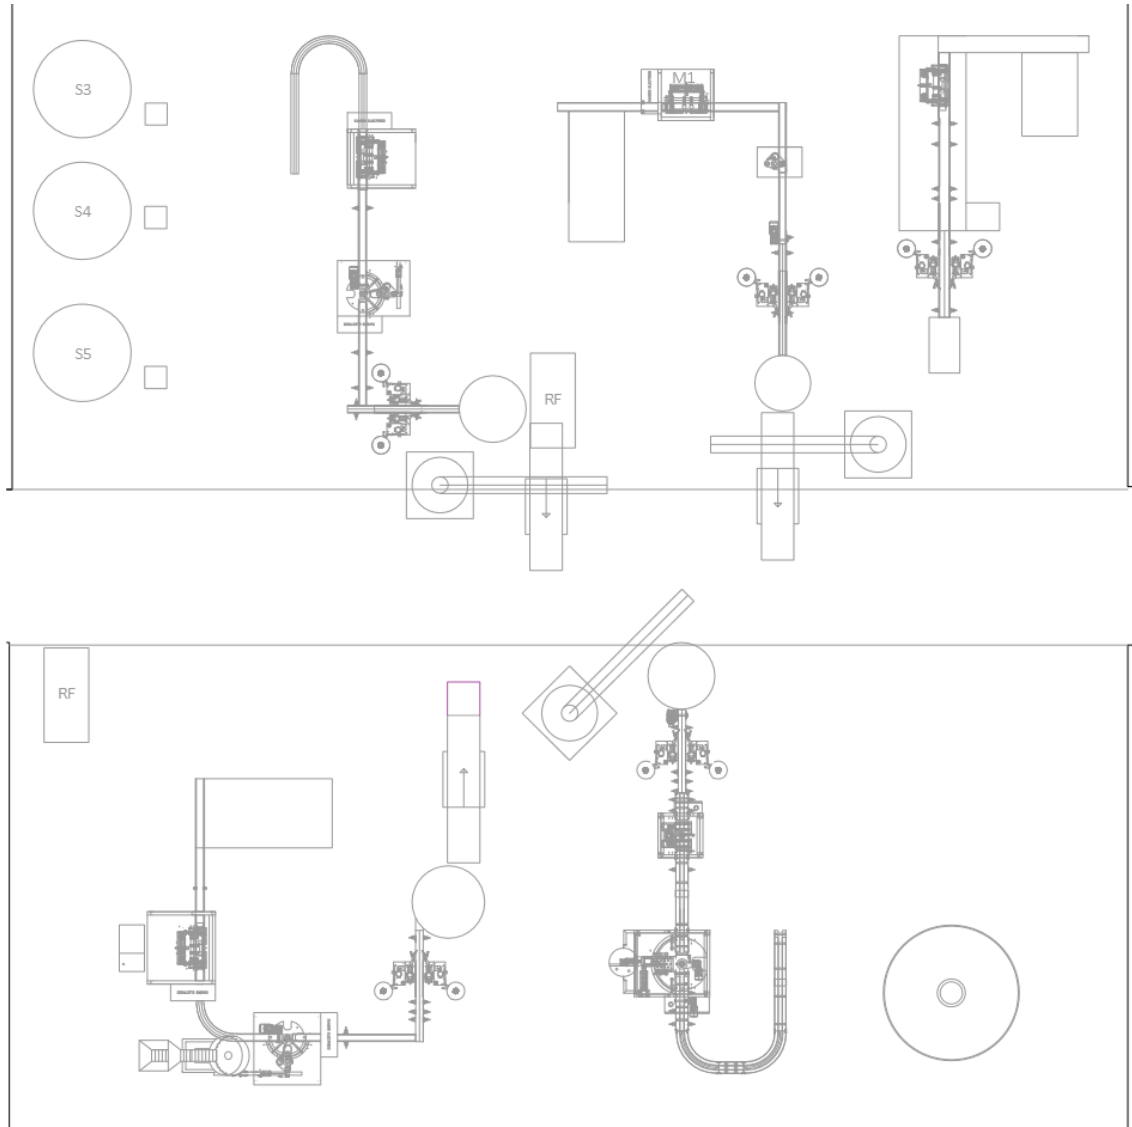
Plano layout de la Nave 11.3 (Fuente: SIPCAM INAGRA S.A.)
